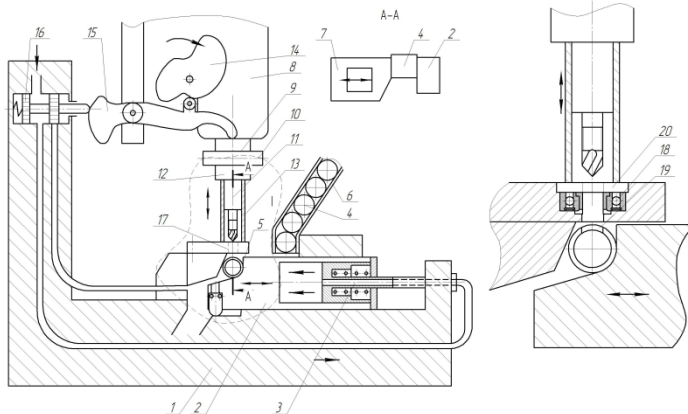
Пневматичний автоматизований пристрій для свердління і нарізання різі в трубчастих заготовках
